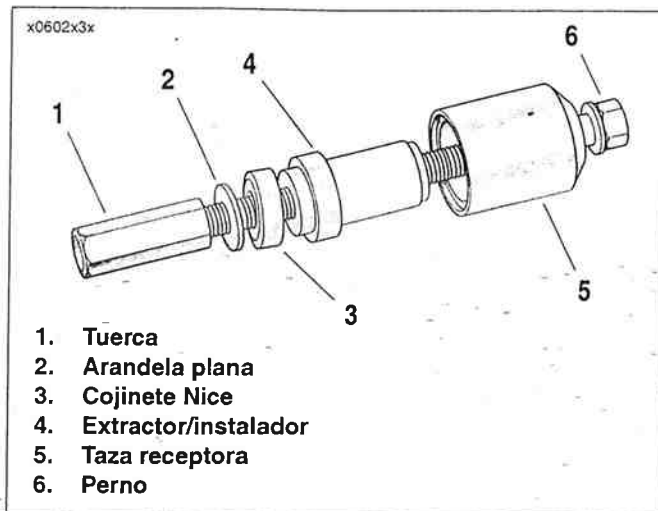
Extractor/instalador de bujes de la biela (HD-95970-32D)
